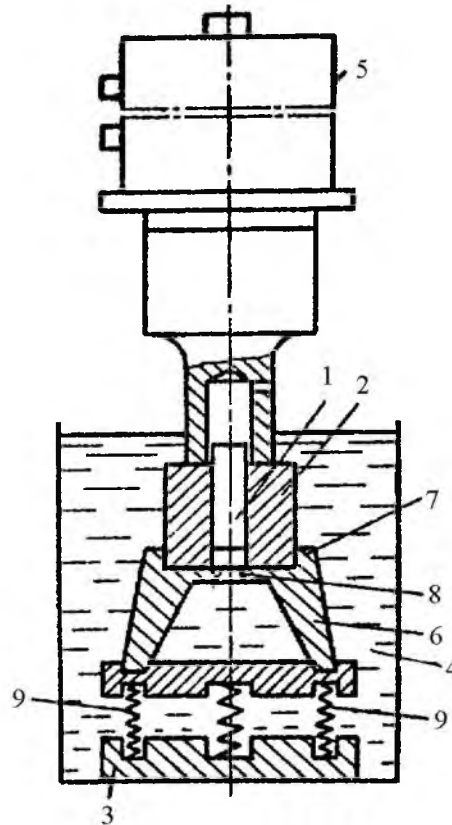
Устройство для ультразвуковой разборки соединения типа вал – втулка: 1 – вал; 2 – втулка; 3 – ванна; 4 – водно-щелочной раствор; 5 – ультразвуковой преобразователь; 6 – упор; 7 – ложемент; 8 – коническое отверстие; 9 – витые цилиндрические пружины
